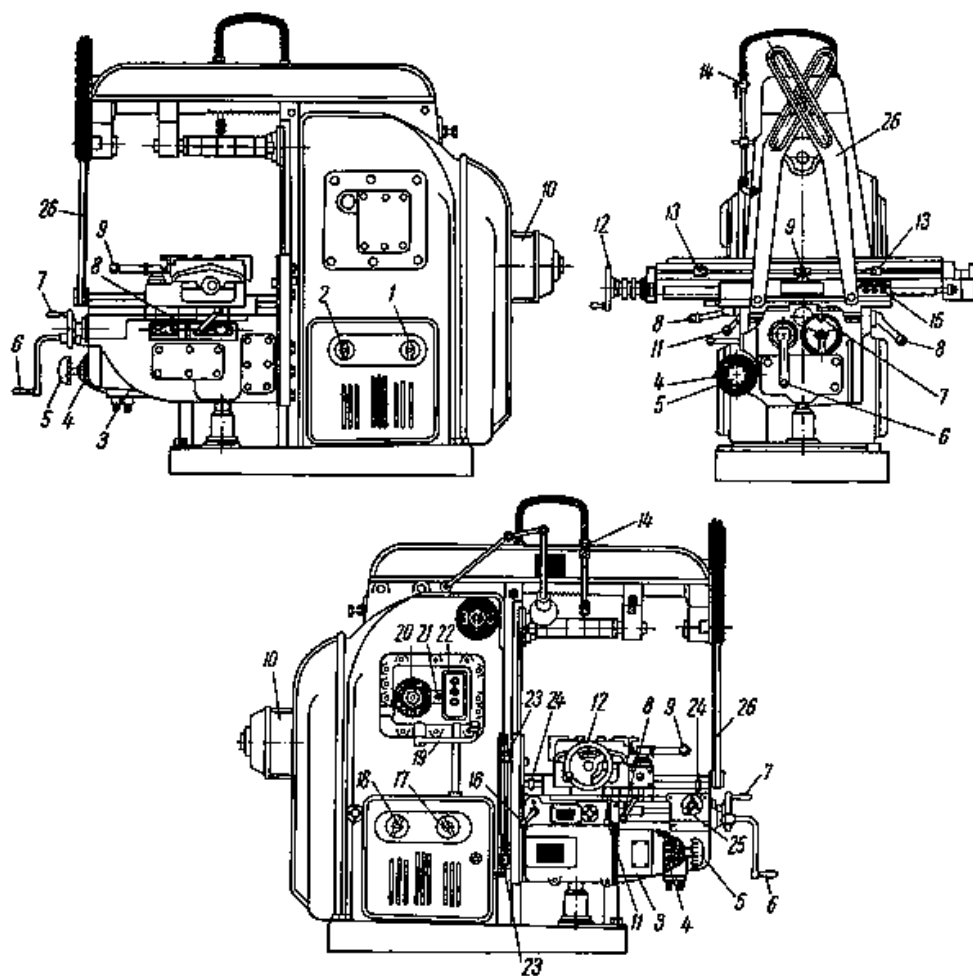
Расположение составных частей горизонтального фрезерного станка 6H82Г
